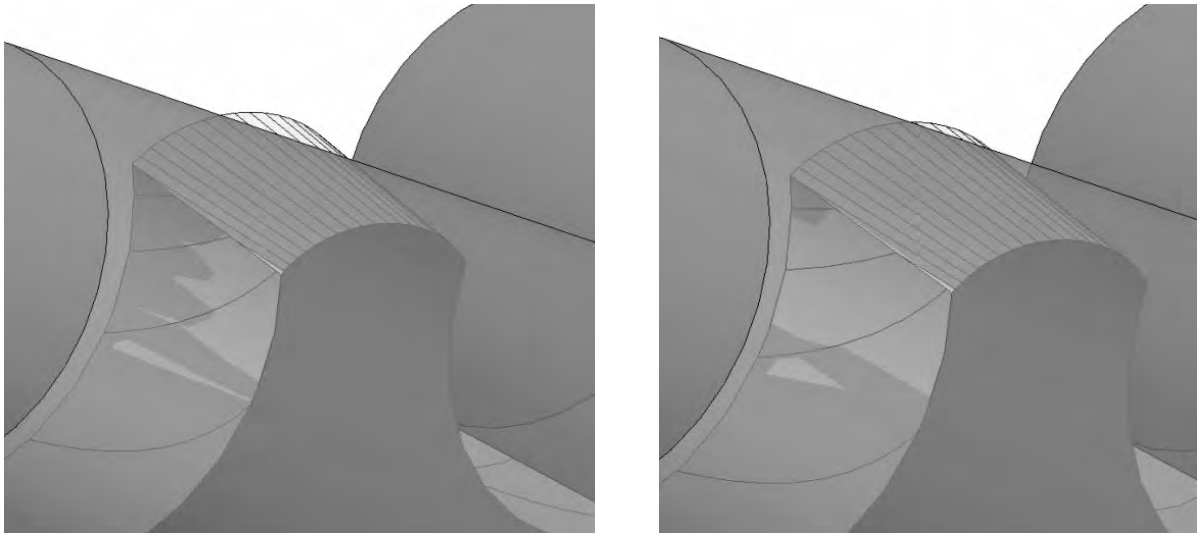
Пятно контакта в прецессионной роликовой передаче с эксцентриковой зубчатой поверхностью сателлитного колеса
